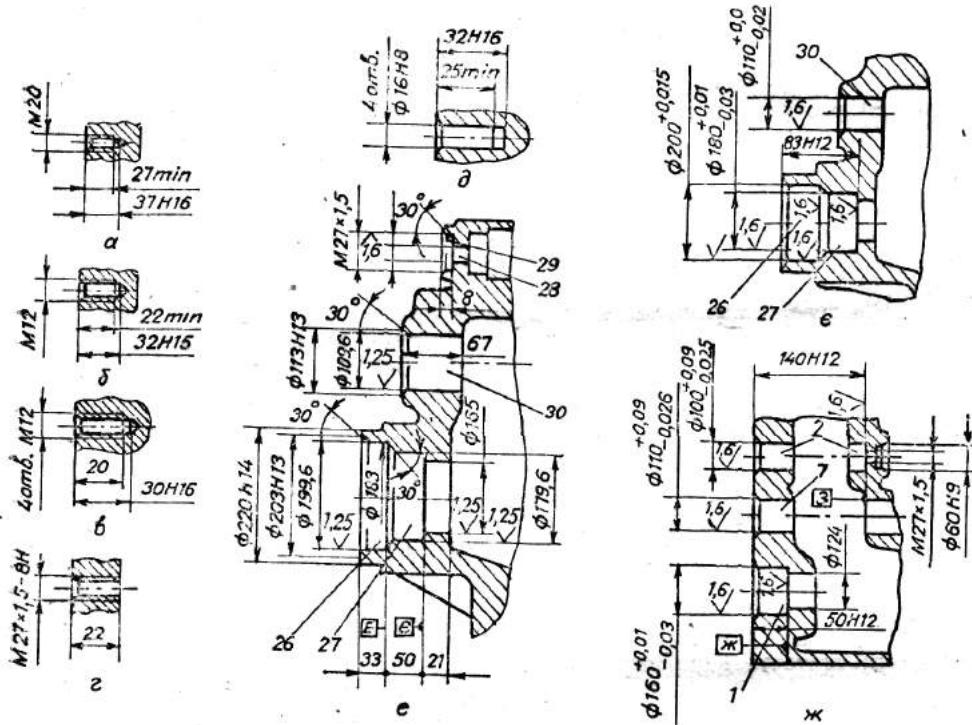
Схеми обробки елементів корпусу редуктора:
